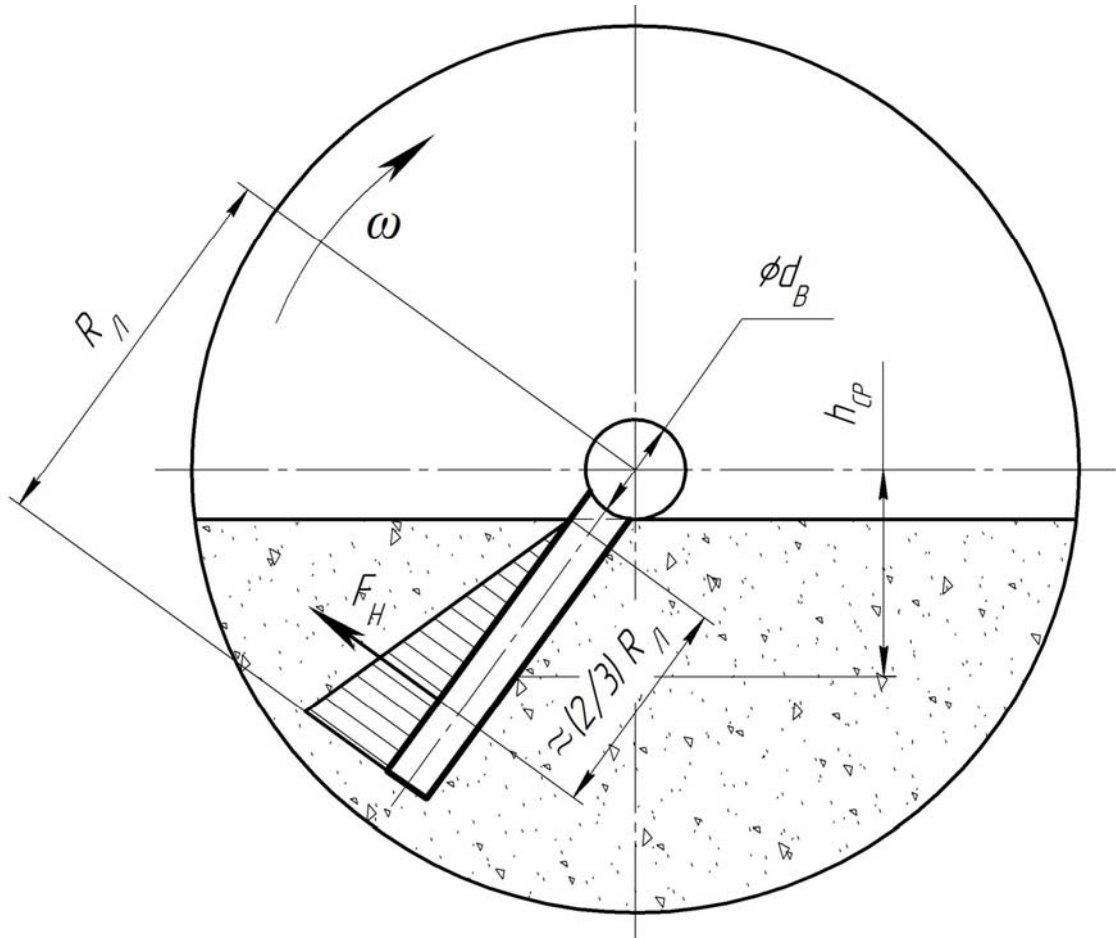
Розрахункова схема лопатевого змішувача
